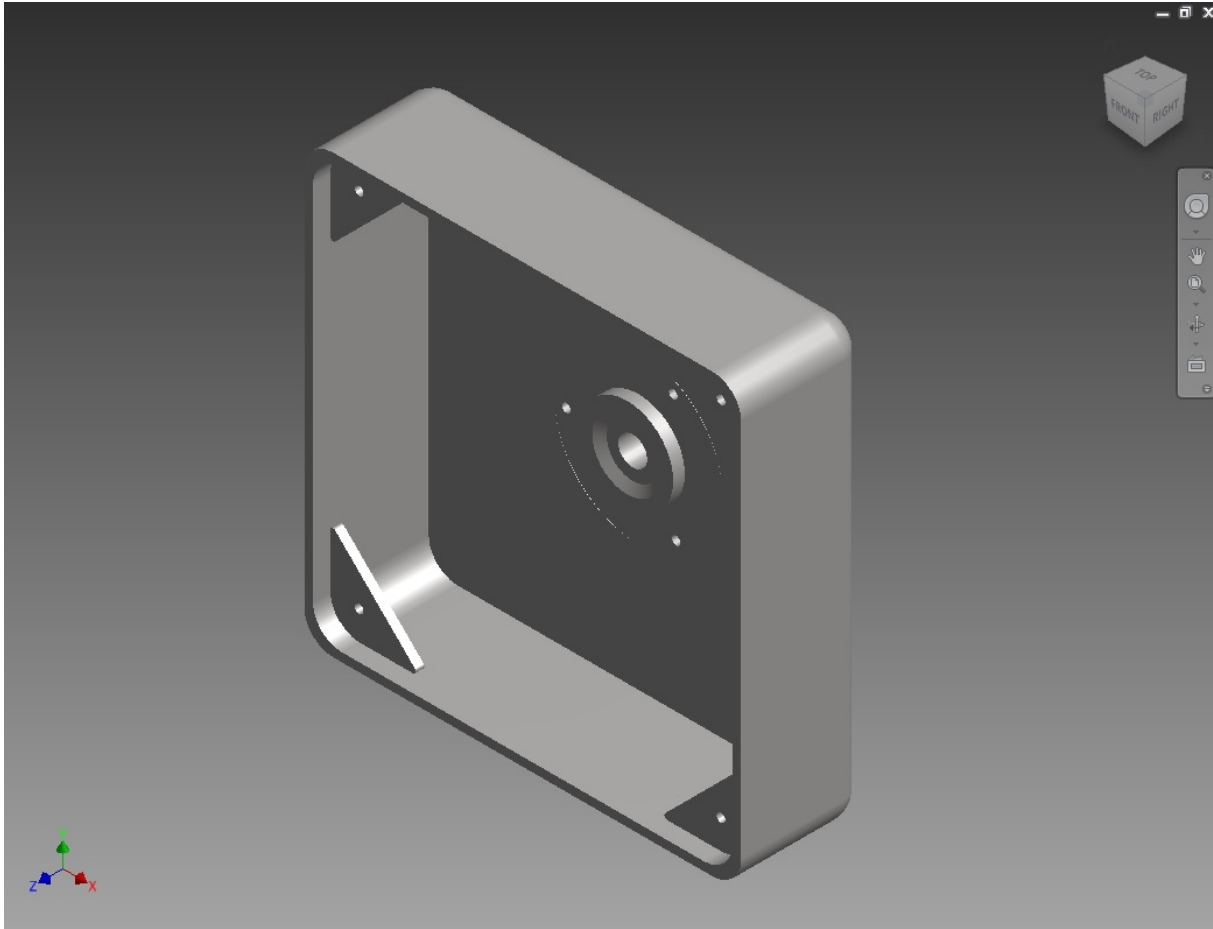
Base soldada con los soportes de la tapa inferior diseñada en CAD
